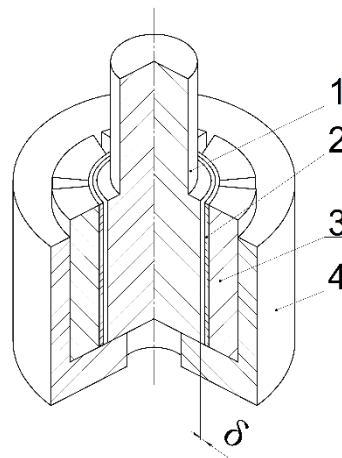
Оснастка для диффузионной сварки катодного узла в сборе:
